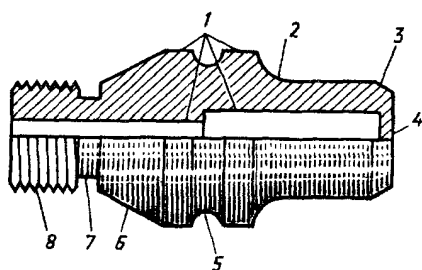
Види поверхонь, які одержують токарною обробкою:
